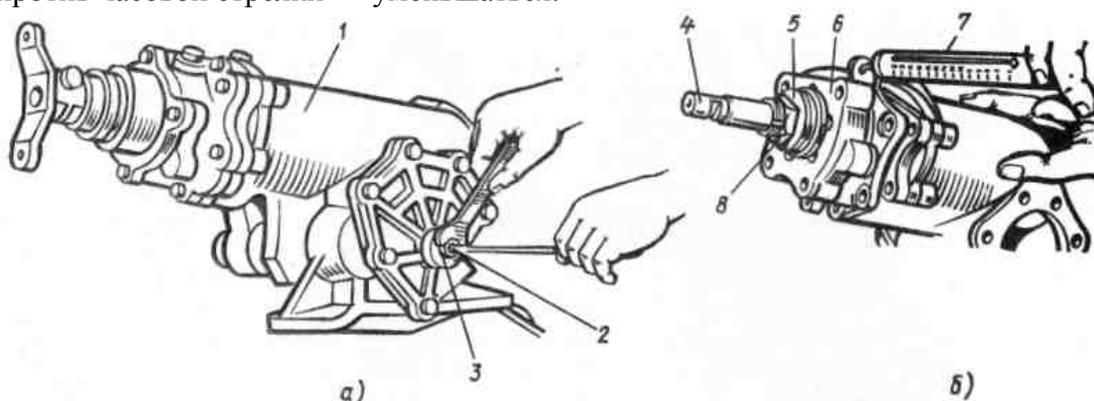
Регулировка рулевого механизма автомобиля ЗИЛ –
